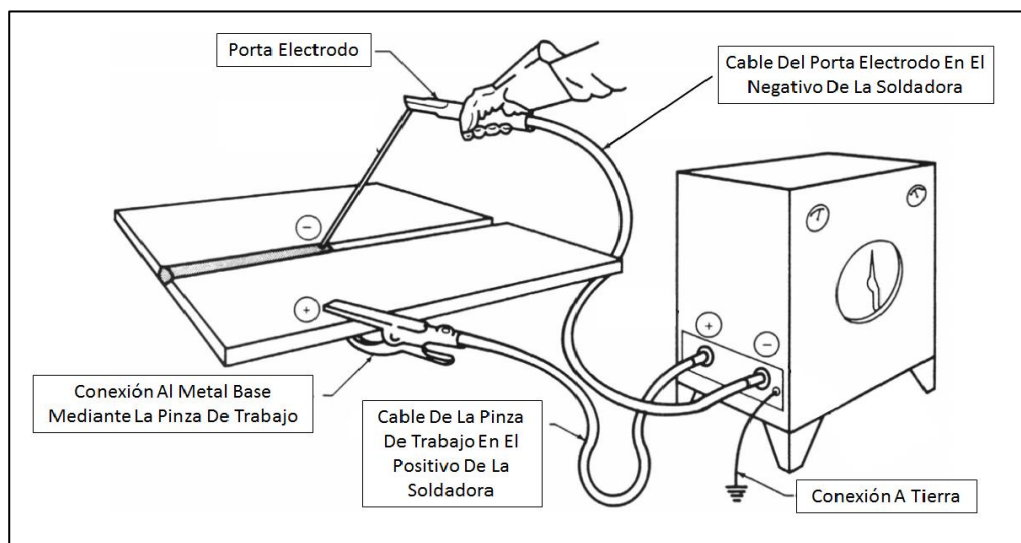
Soldadura En Polaridad Directa [3]
